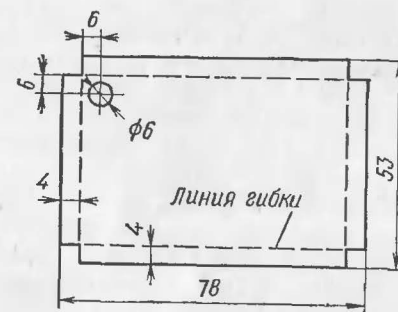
Крышки корпуса усилителя (в нижней крышке отверстие не выполнять)
